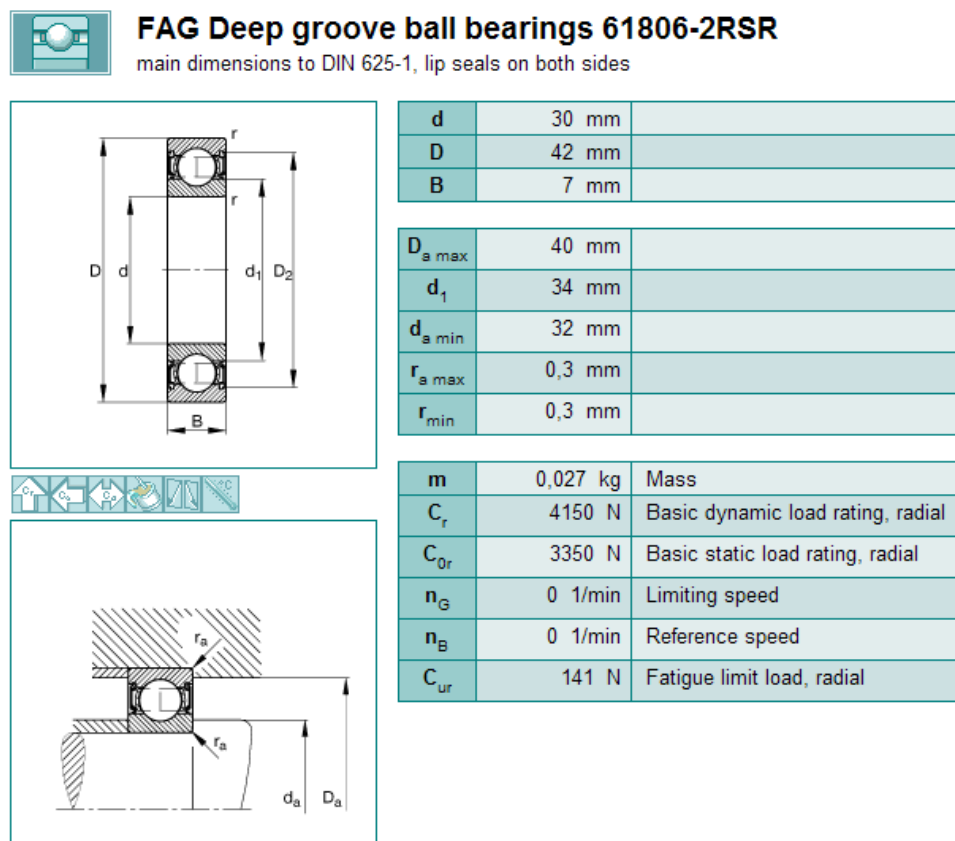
Dimensões e características mecânicas do rolamento 61806, [10].
